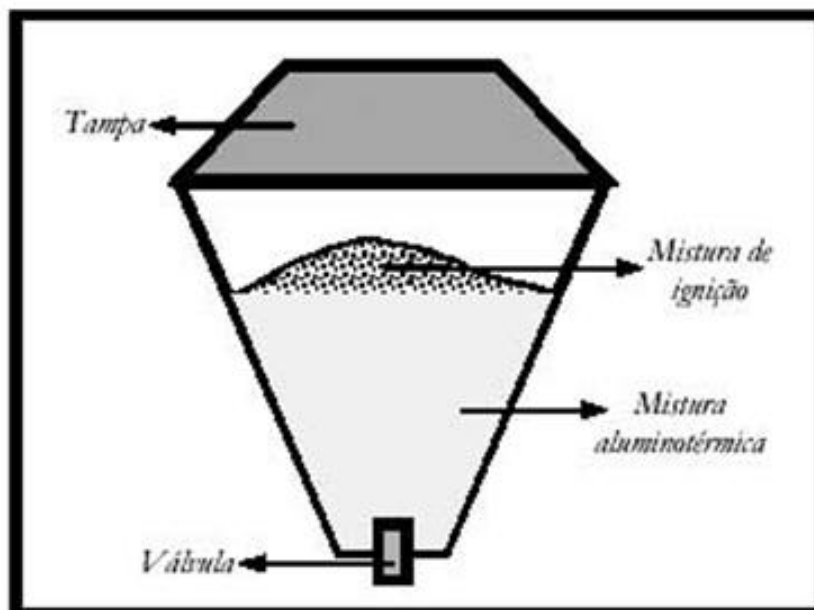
Cadinho utilizado no processo de soldagem aluminotérmica.
